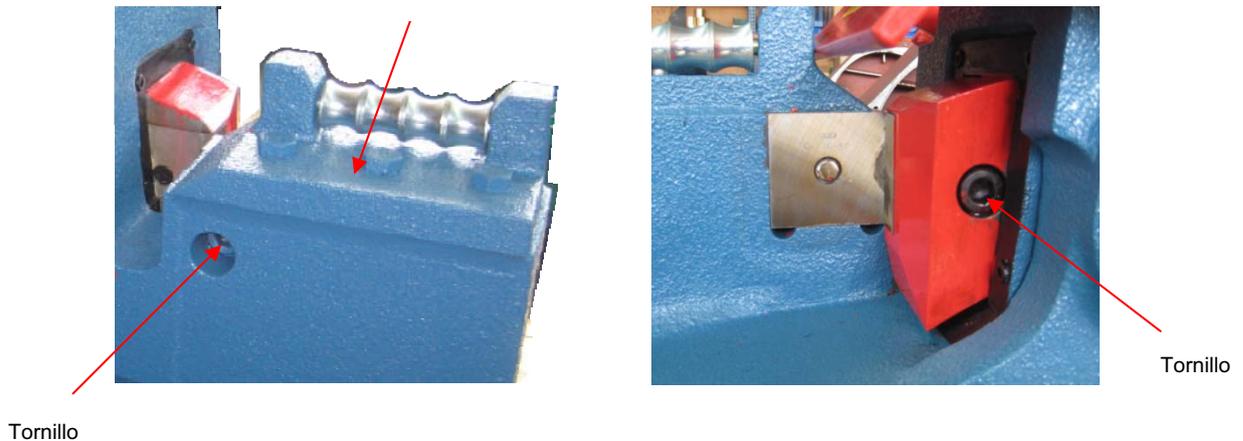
Soporte de Roldanas y tornillo de la cuchilla
